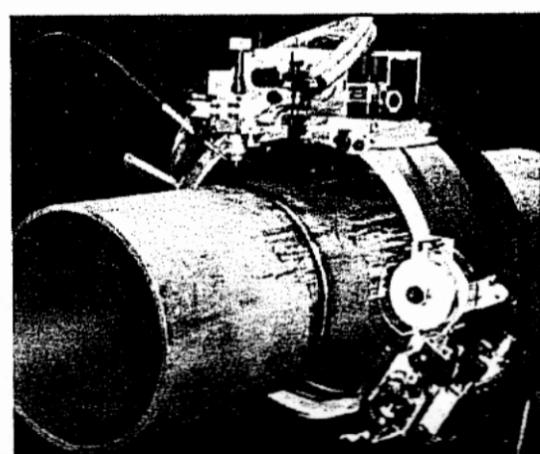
Сварочная головка для труб среднего и большого диаметра
